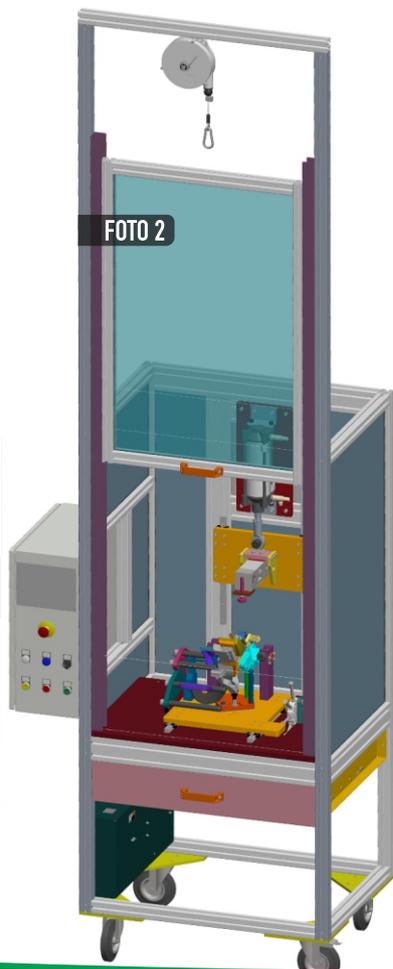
POSTAZIONE SCALDACIABATTE – FOTO 2 BANCO CONTROLLO LEVA SGANCIO – FOTO 3 POSTAZIONE RIBADITURA – FOTO 4 BANCO ASSEMBLAGGIO PEDALIERE
